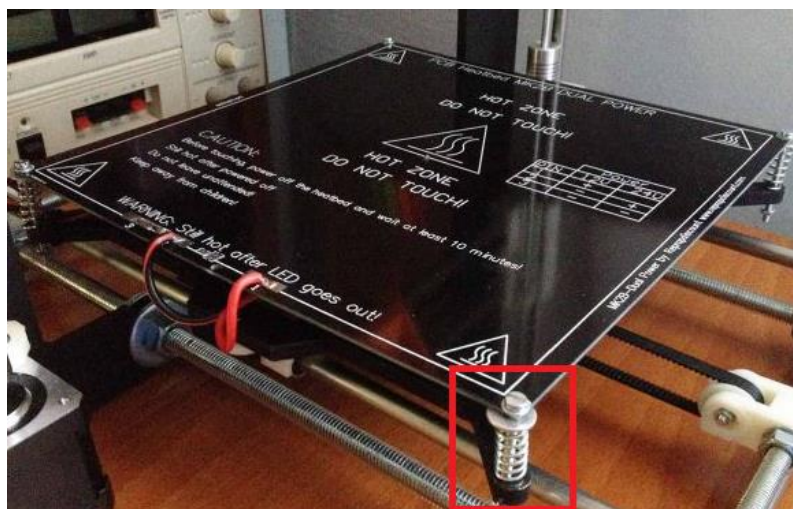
Sistema de anclaje a la plataforma móvil. Manual de montaje PCB. Zona maker por Raúl Diosdado.
